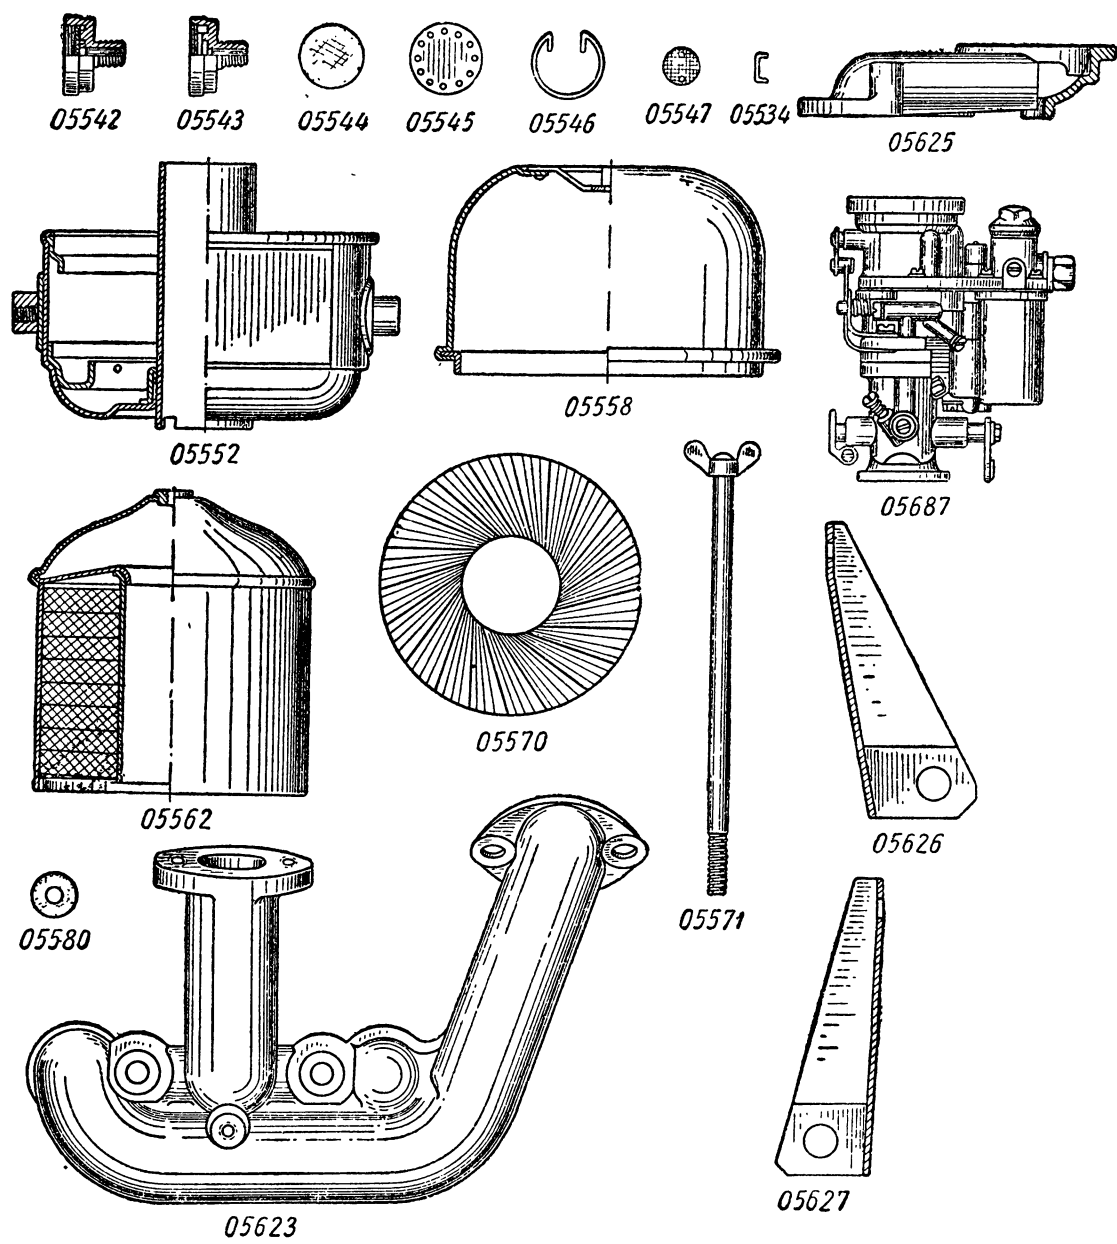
Установка воздухоочистителя с карбюратором пускового двигателя.
